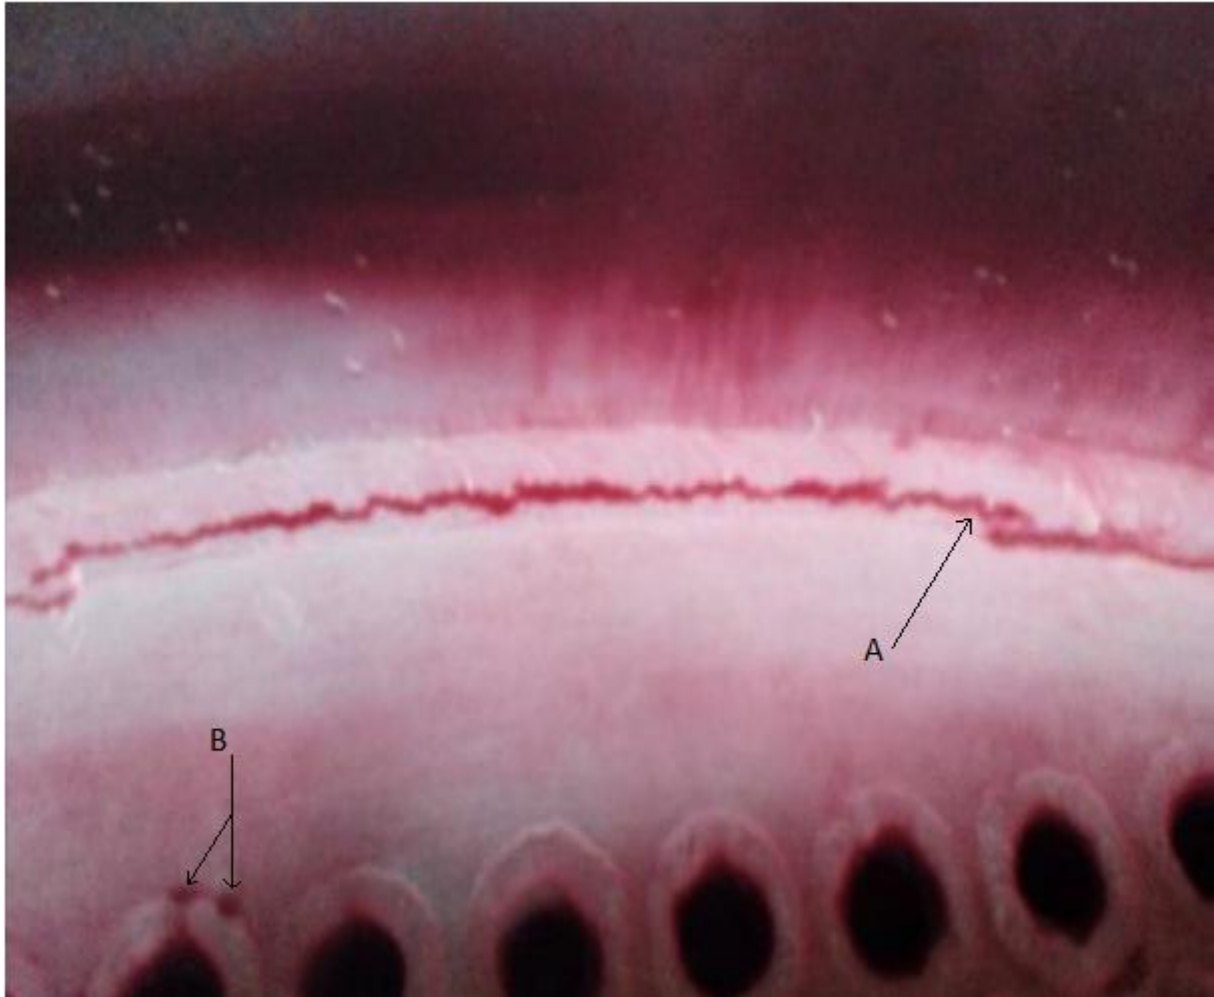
Le contrôle par ressuage montre l'ampleur de la fissure sur joint soudure plaque supérieur avec virole (A) et on peut remarquer aussi certaines fissures sur joints des soudures tube avec plaque (B).
